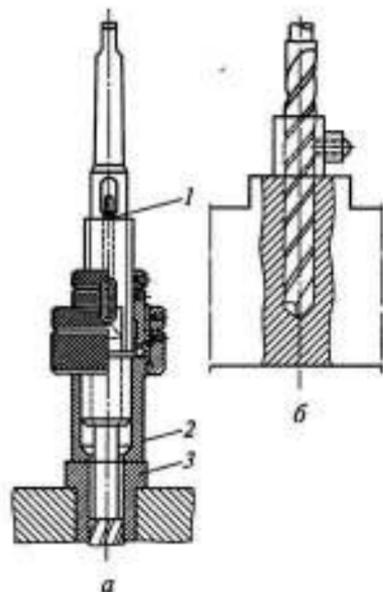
Приспособление для ограничения движения подачи шпинделя: а — патрон с регулируемым упором; б — упорное кольцо; 1 — корпус патрона со сверлом; 2 — упорная втулка; 3 — кондукторная втулка.
